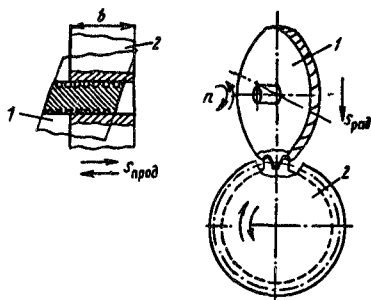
Схема параллельного шевингования цилиндрического зубчатого колеса
